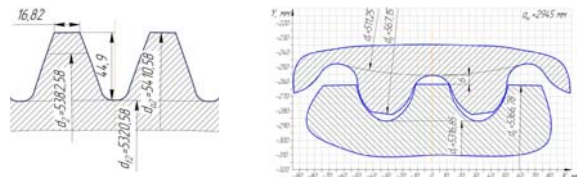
Эвольвентный профиль колеса и профили зацепления Новикова
